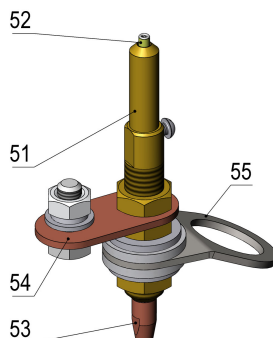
Горелка для сварки под слоем флюса
